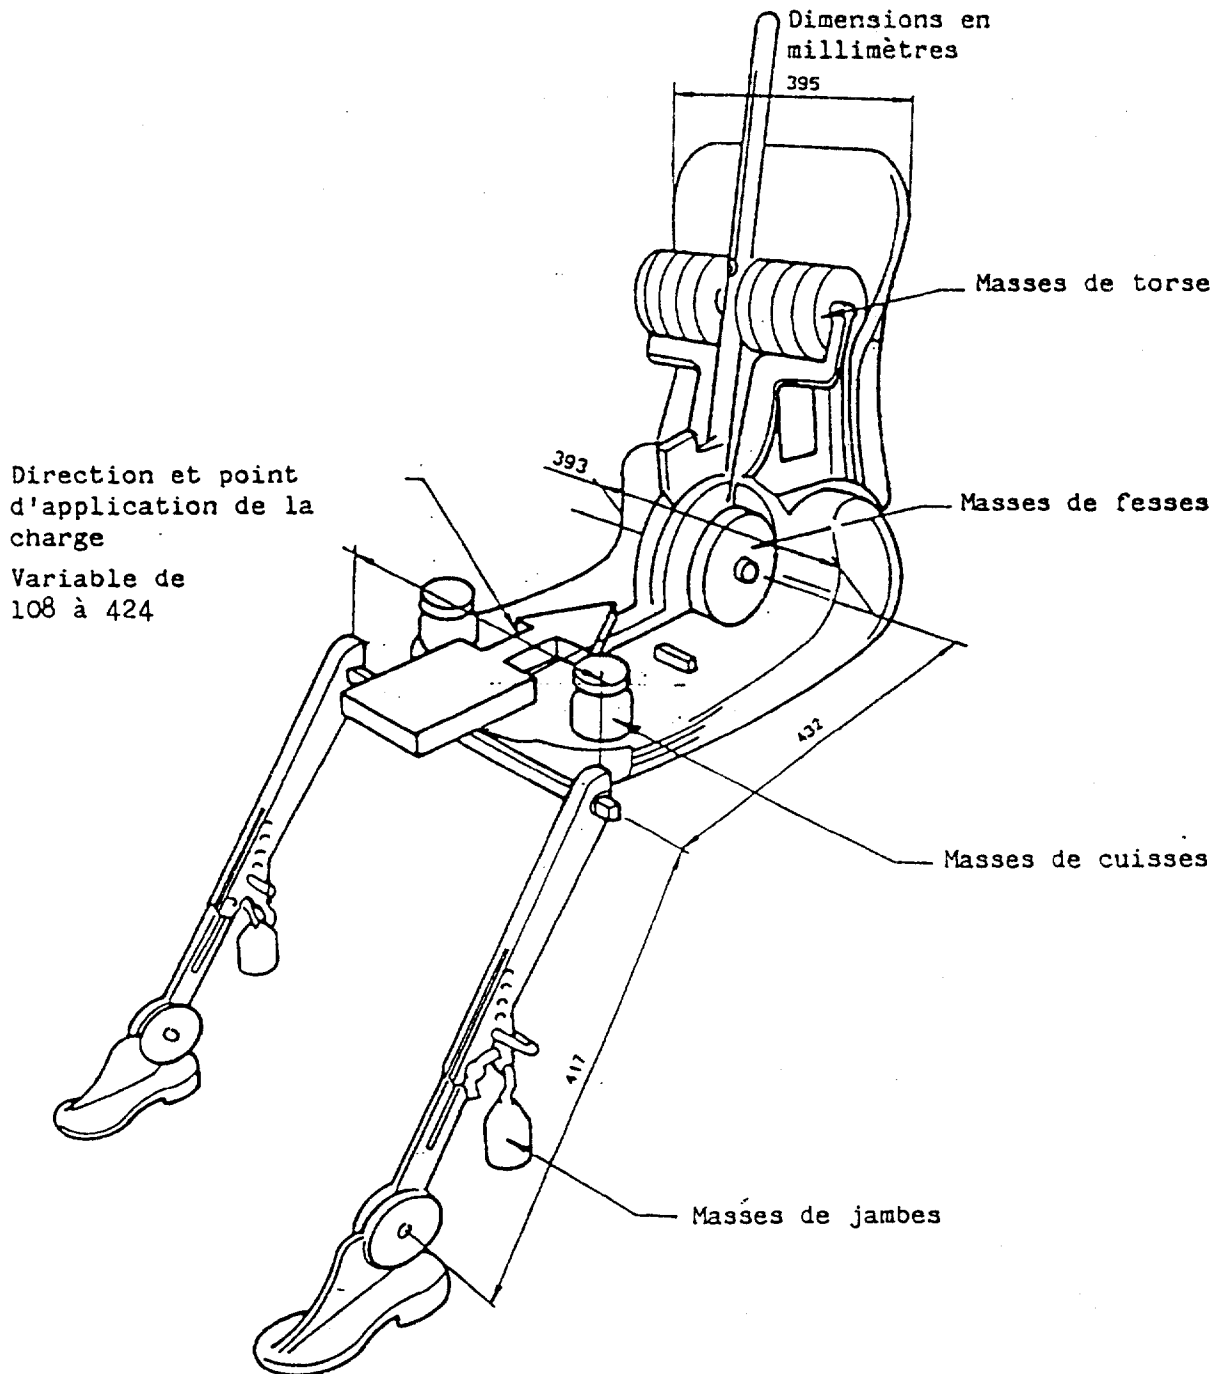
Dimensions des éléments de la machine 3-D H et emplacement des masses
